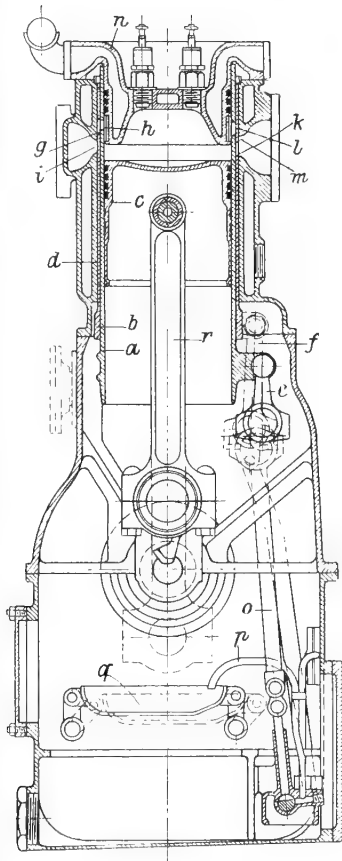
Schnitt durch einen Knight-Schiebermotor.
